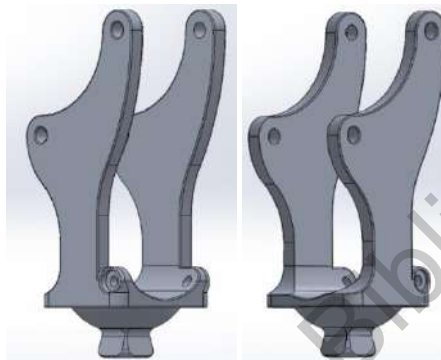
Diseño final de la componente inferior de la rodilla (eslabón 'd').
